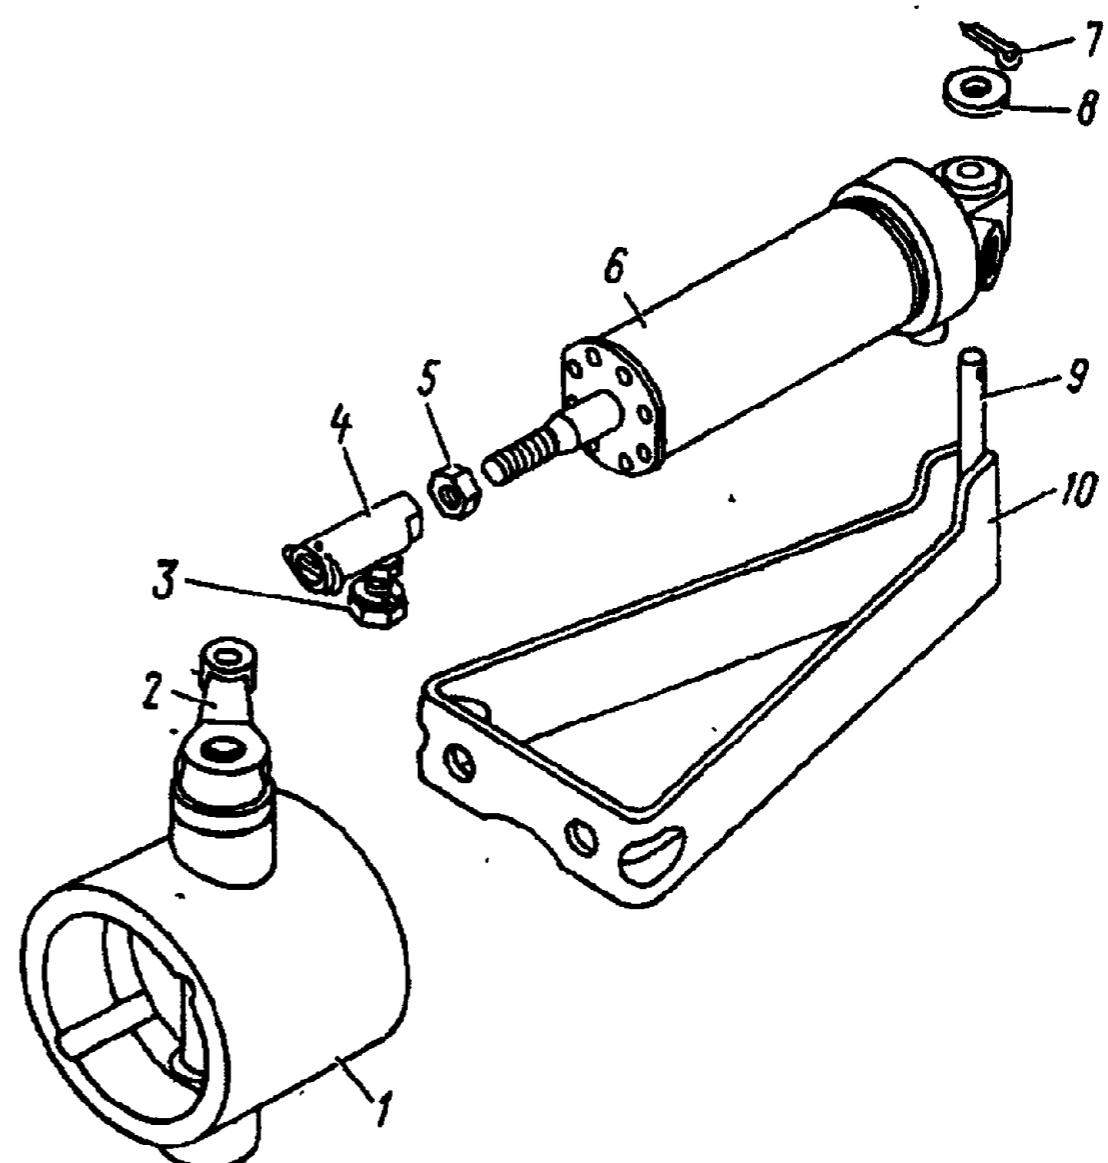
Установка пневматического цилиндра вспомогательной тормозной системы:
